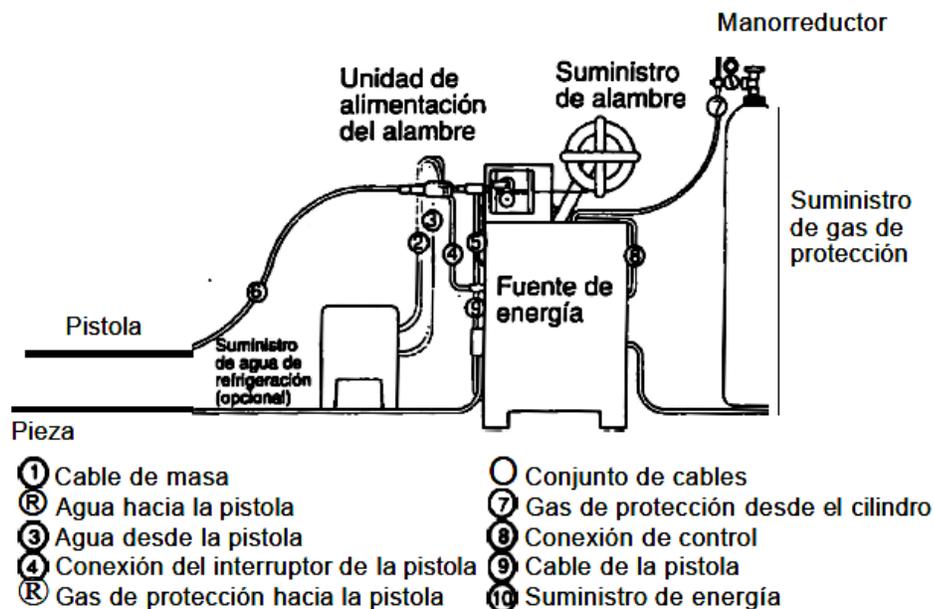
Equipo para soldadura MIG/MAG
